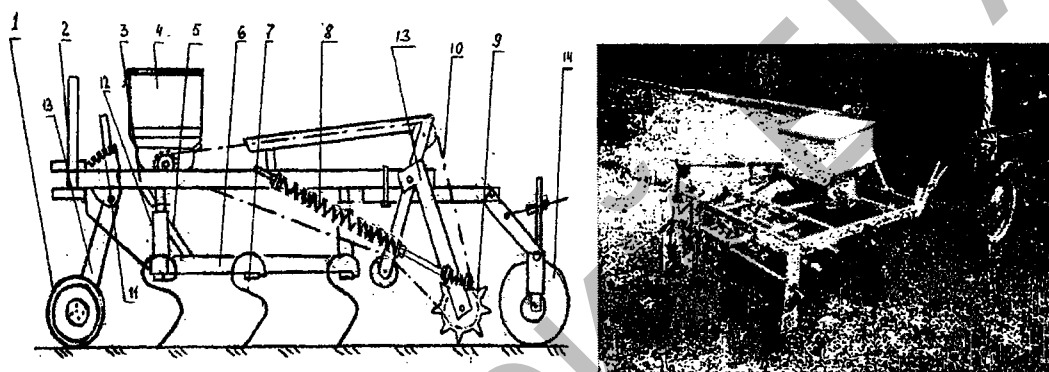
Схема комбинированного почвообрабатывающего агрегата:
